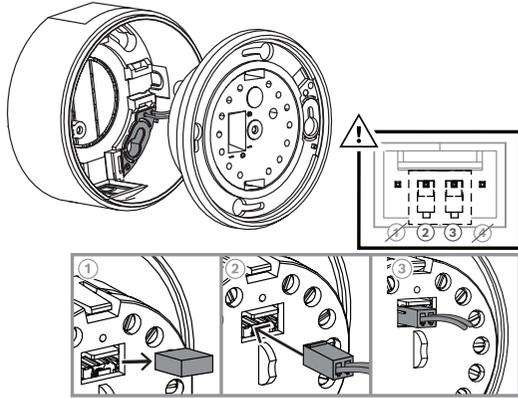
Collegamento di un singolo contatto anti-manomissione da parete
